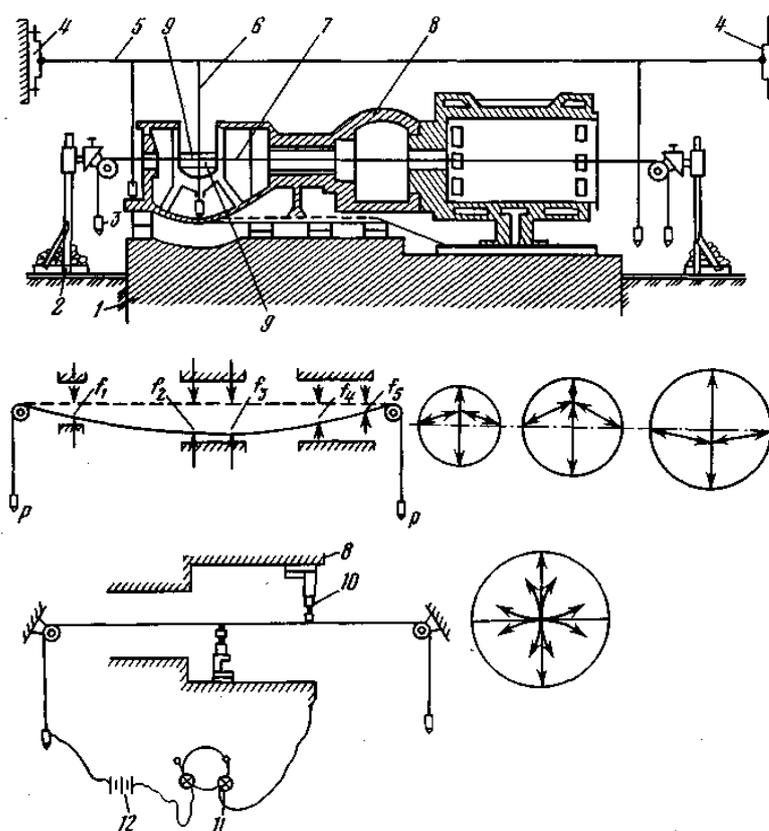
Схема выверки положения главных осей оборудования ГКС при помощи струны: 1 – фундамент, 2 – подставка, 3 – груз, 4 – скоба, 5 и 7 – струны, 6 – отвес, 8 – рама, 9 – деревянные плашки, 10 – штихмас, 11 – сигнальная лампа, 12 – источник питания [31]
